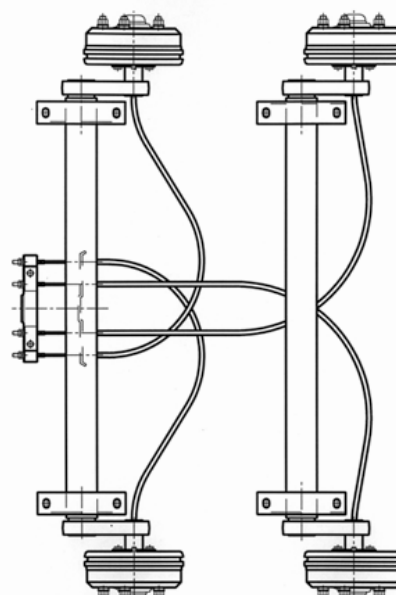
Montaje de la vigueta de elevación en tándem
